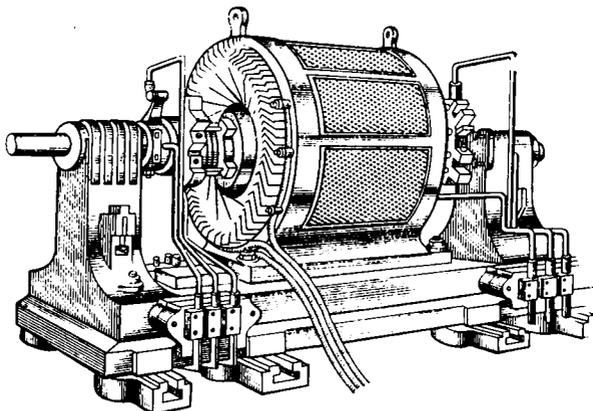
Асинхронный двигатель, изготовленный для Франкфуртской выставки
